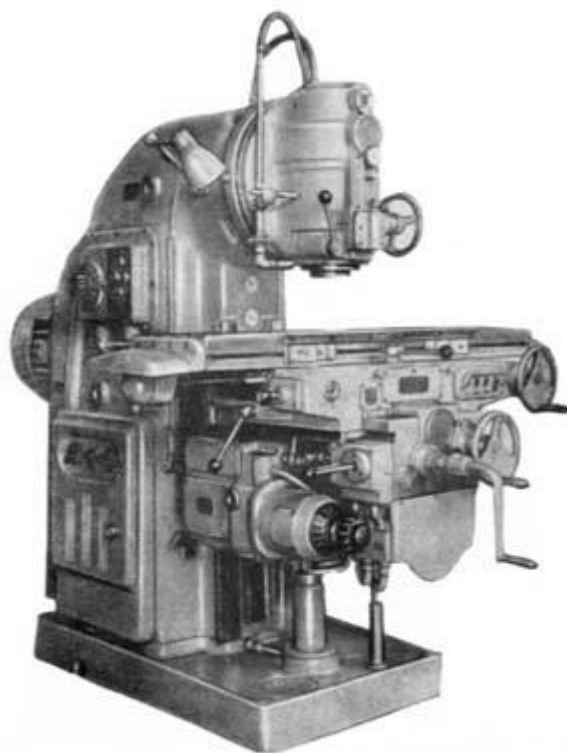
6М12П станок консольно-фрезерный вертикальный с поворотной головкой.
